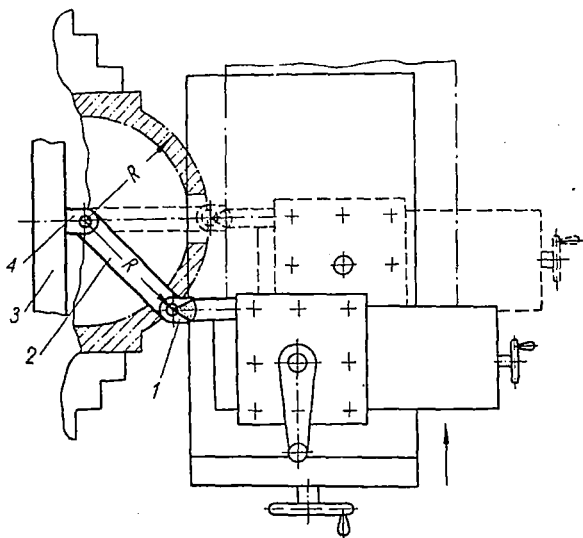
Приспособление для обработки выпуклых сферических поверхностей больших радиусов.
